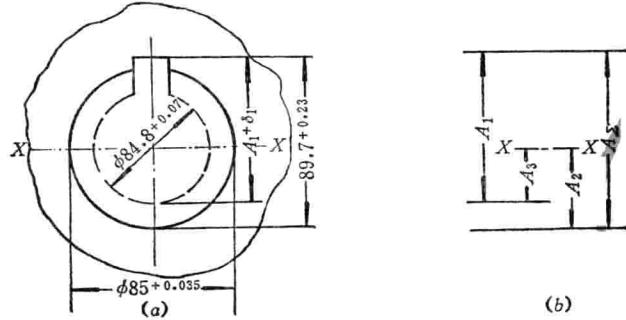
齿轮基准孔与键尺寸的工艺尺寸换算
